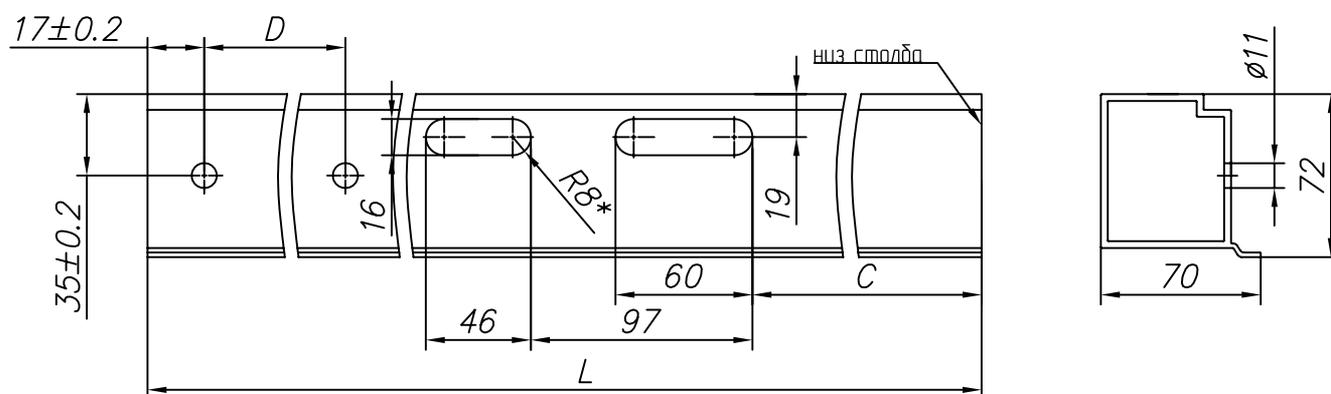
Изготовление столба притвора с пазом для ответной пластины замка для калитки с левым открыванием
